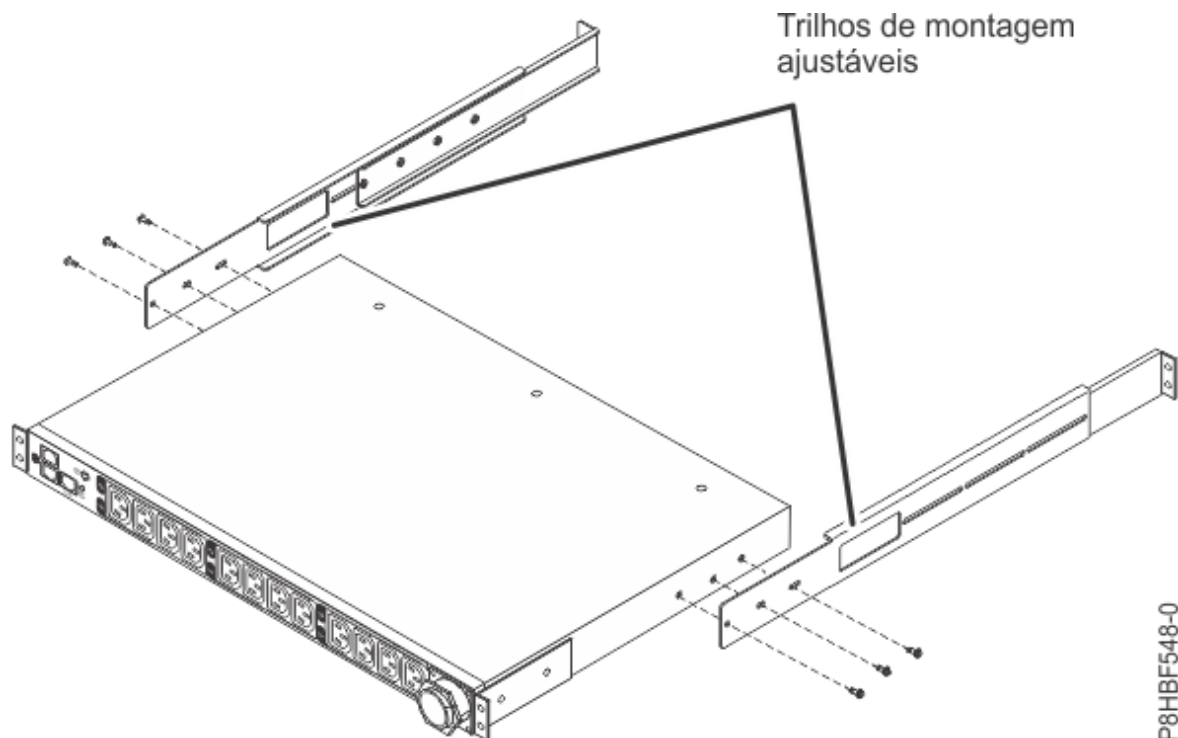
Conectando os trilhos de montagem ajustáveis ao chassi de PDU Alternada inteligente
